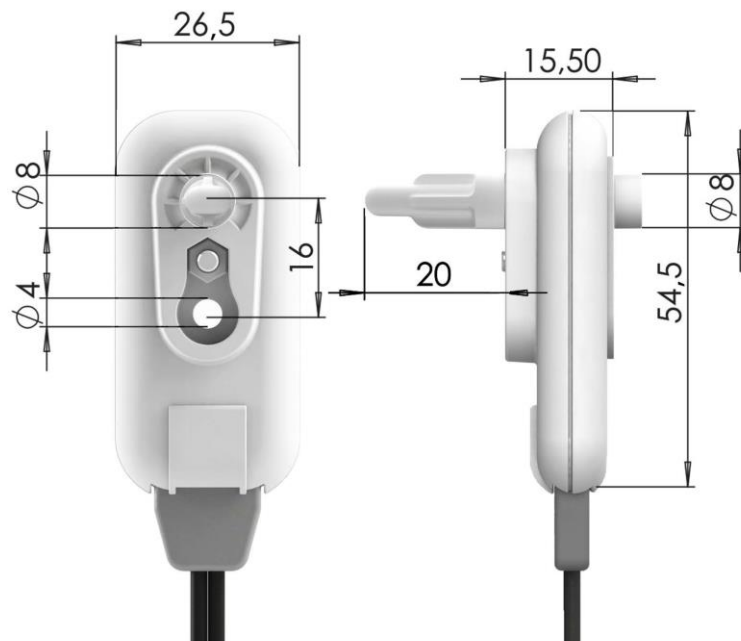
Внешний вид и габаритные размеры датчика ВОД
